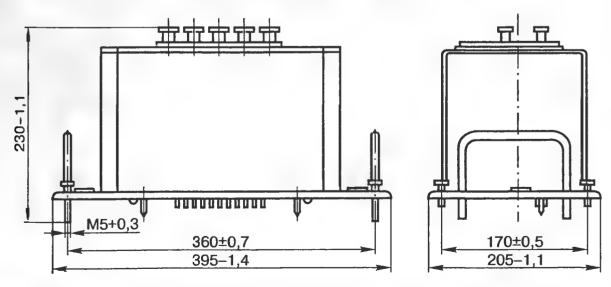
Габаритные и установочные размеры блоков БСКЛ, ТПЧЛ, ФАЛ
